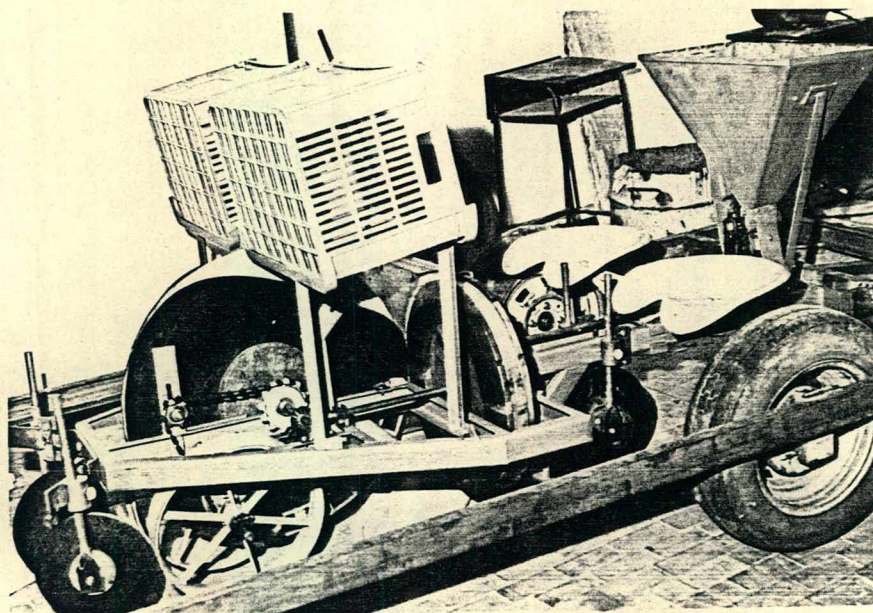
Aspecto final após a montagem dos assentos e do adubador.
